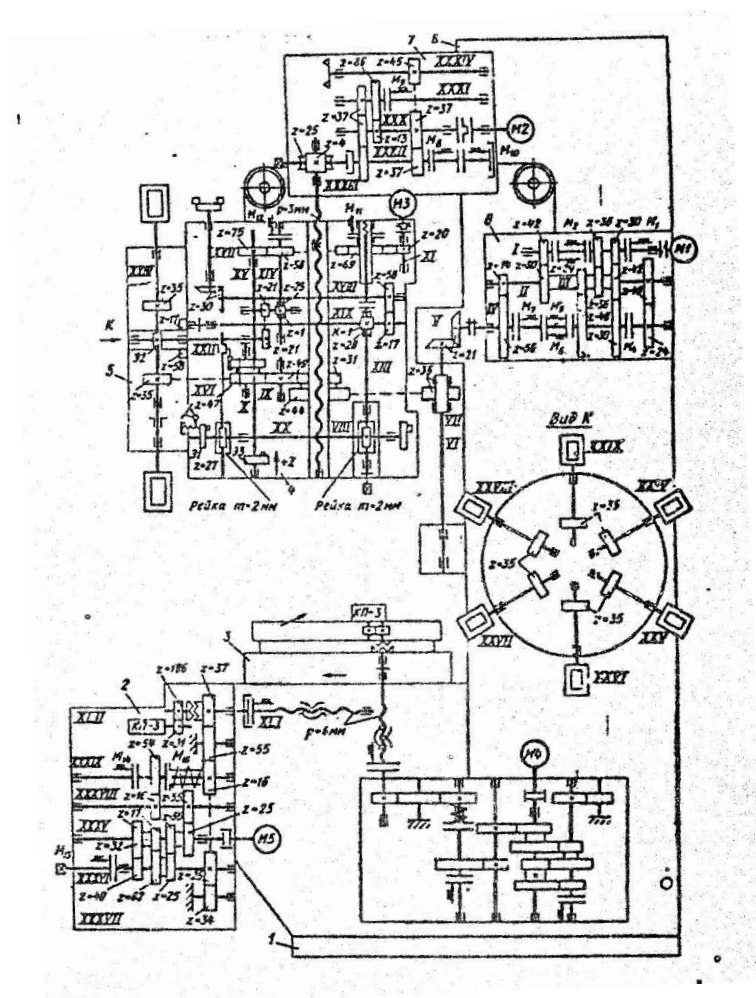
Кинематическая схема станка 2A135Ф2
